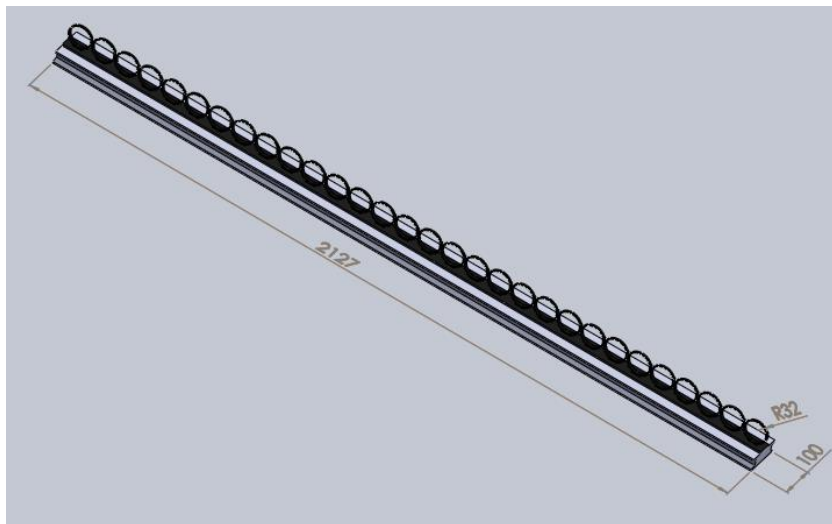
Desenho tridimensional do posicionador de tubos.
